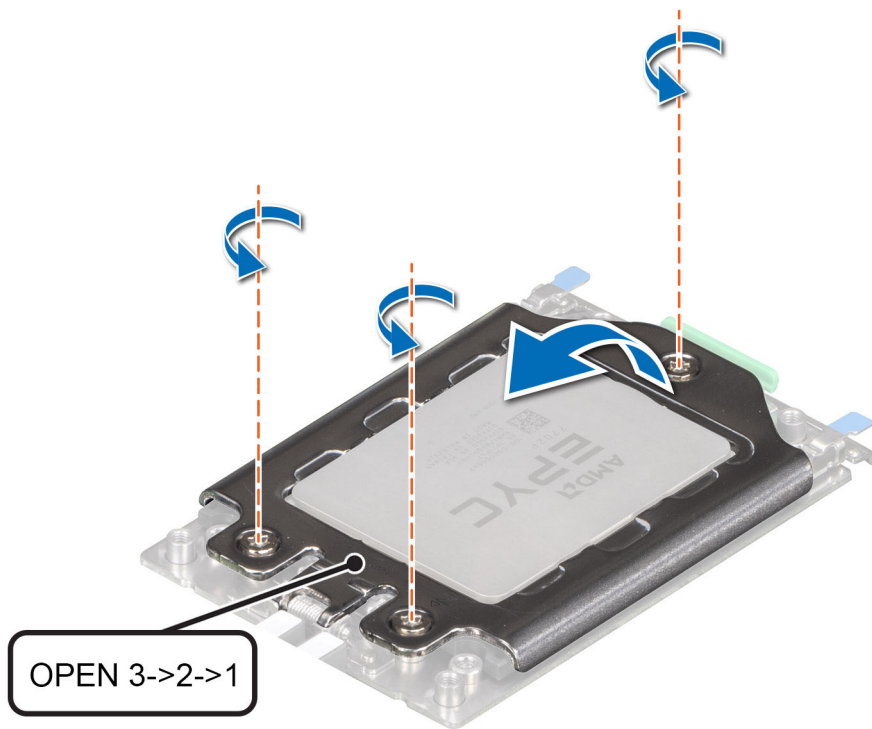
Entfernen der Schrauben auf der Kraftplatte
